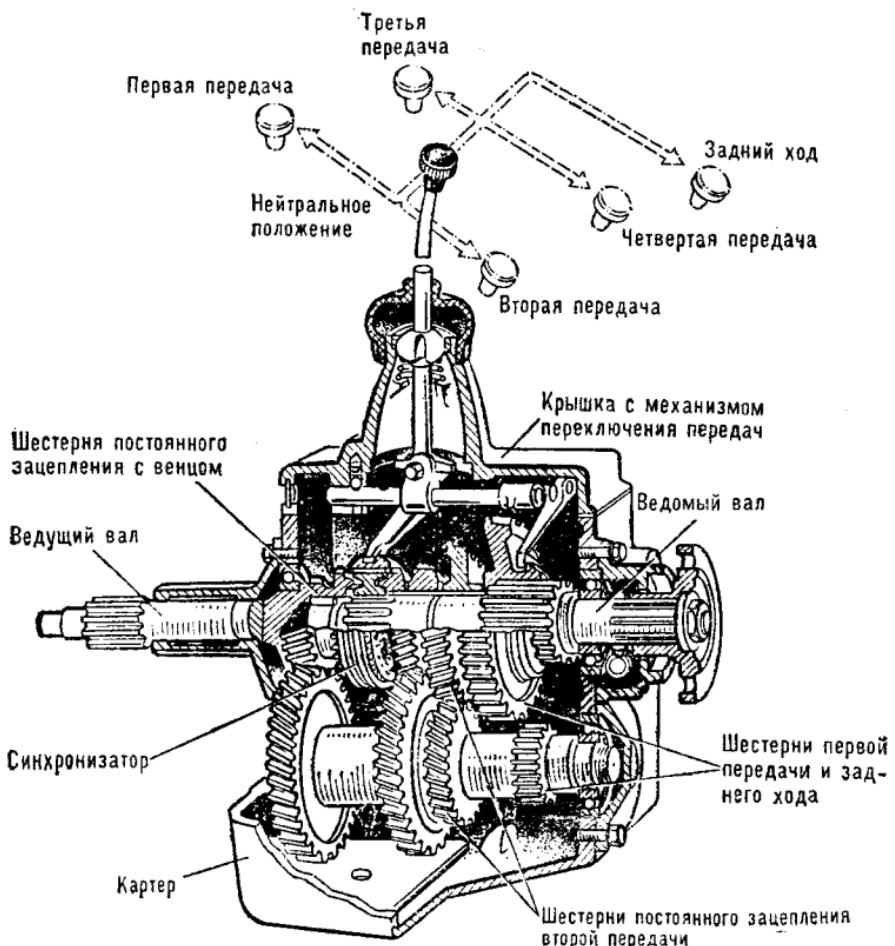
Коробка передач автомобиля ГАЗ-53-12
